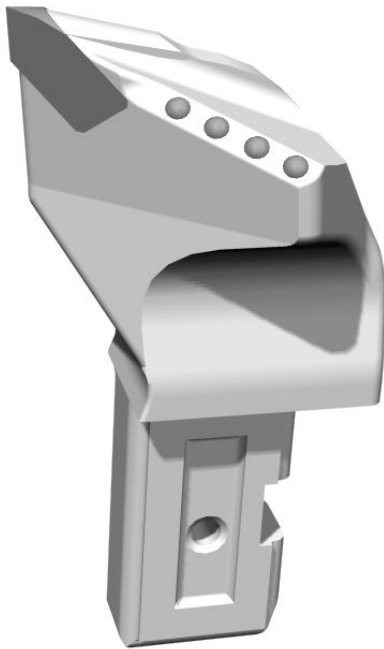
Вид реза с рабочей боковой гранью – резец типа ЗРБ.
